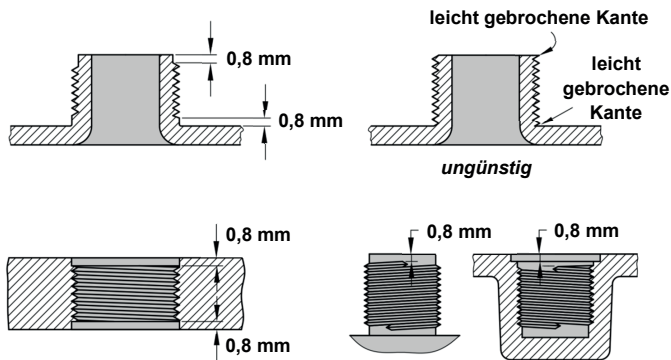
Begrenzung der Gewindelänge in Bezug zum Spritzgussteilrand
